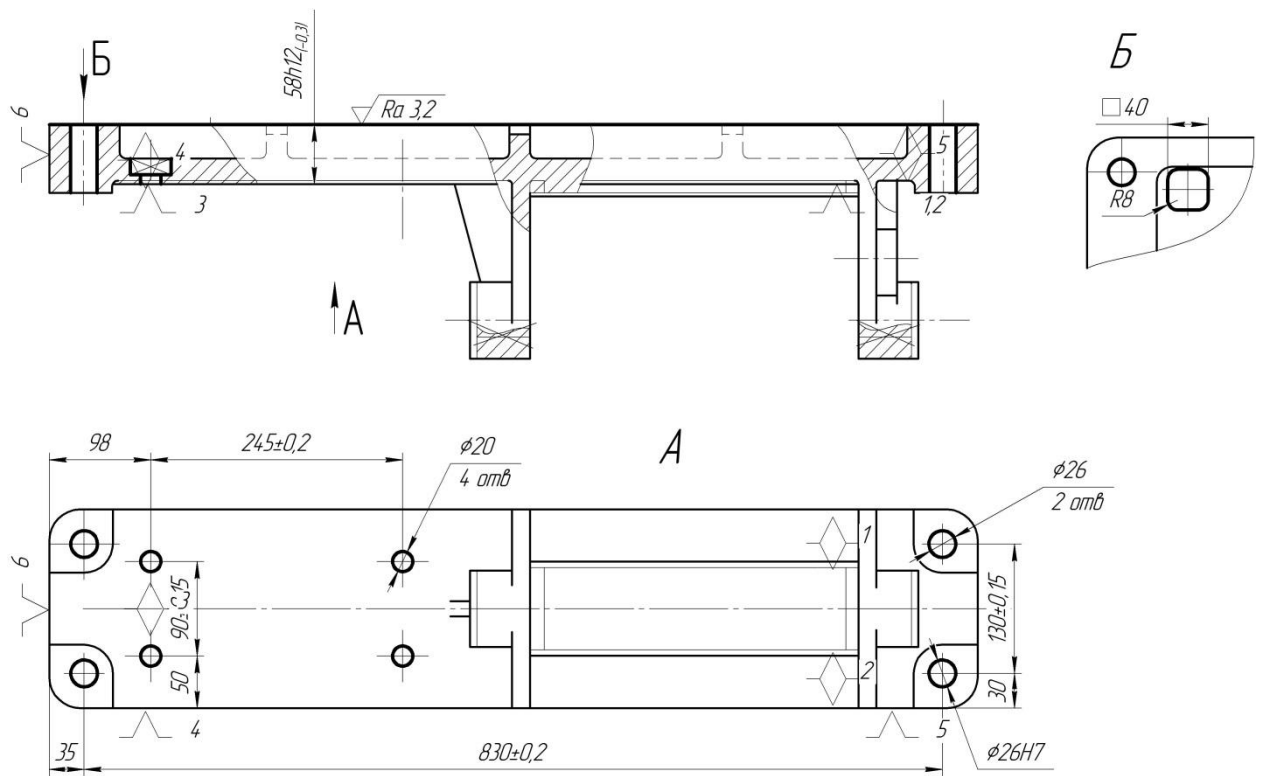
Базування заготовки при обробці на операції 005
